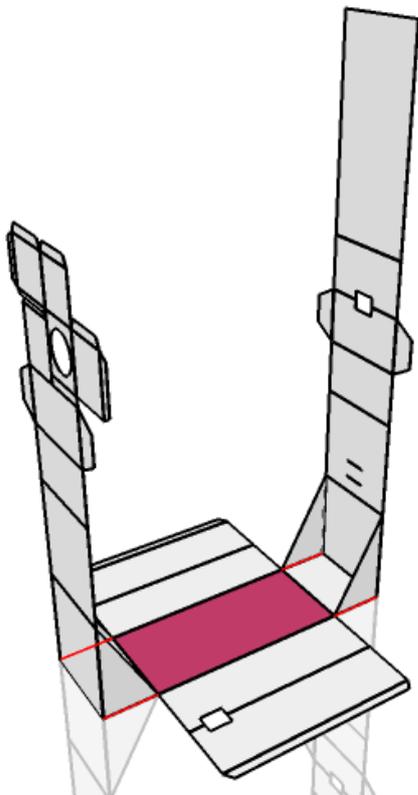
Guía de plegado. Plegado tapas 3. Fuente: Elaboración propia.
